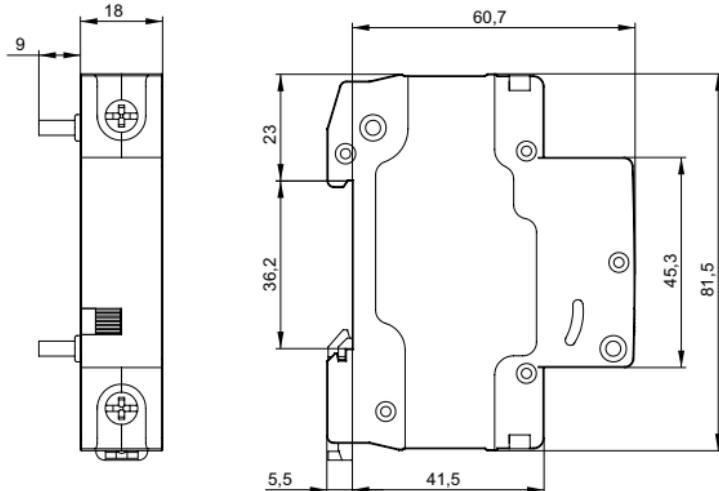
Габаритные размеры PMM47 / Figure 1 – Overall dimensions of RMM47
